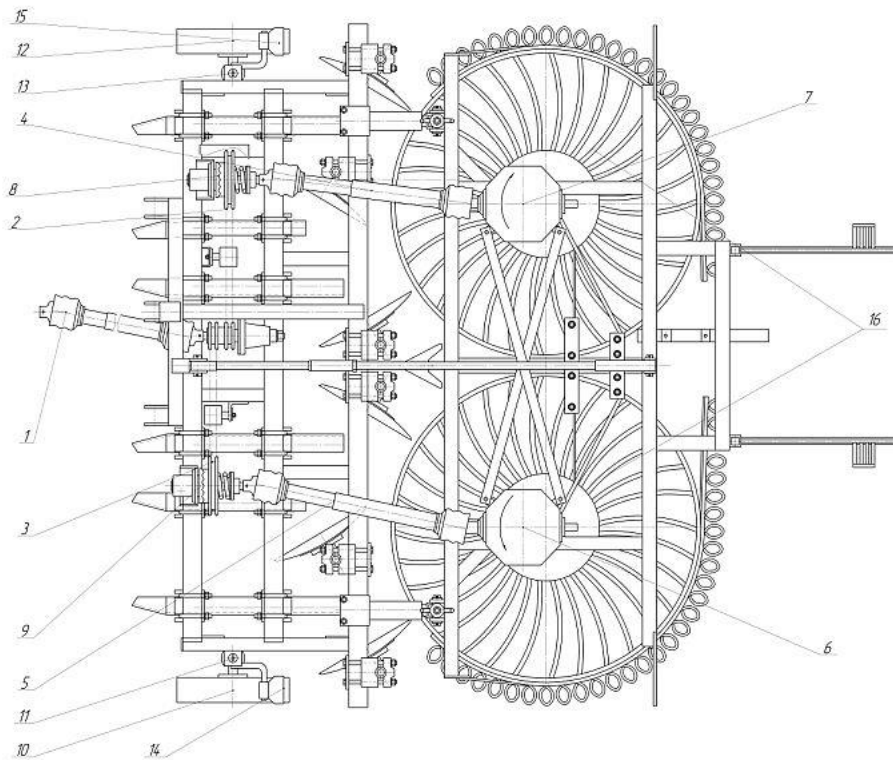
Схема копача АЗБ-6 (вид зверху): 1 – вал карданний; 2, 3 – передачі ланцюгові; 4, 5 – карданні контрприводу турбін; 6, 7 – конічні редуктори; 8, 9 – муфти; 10, 12 – опорні колеса; 11, 13 – механізм регулювання положення коліс; 14, 15 – чистики; 16 – турбінні очисники-підбирачі
